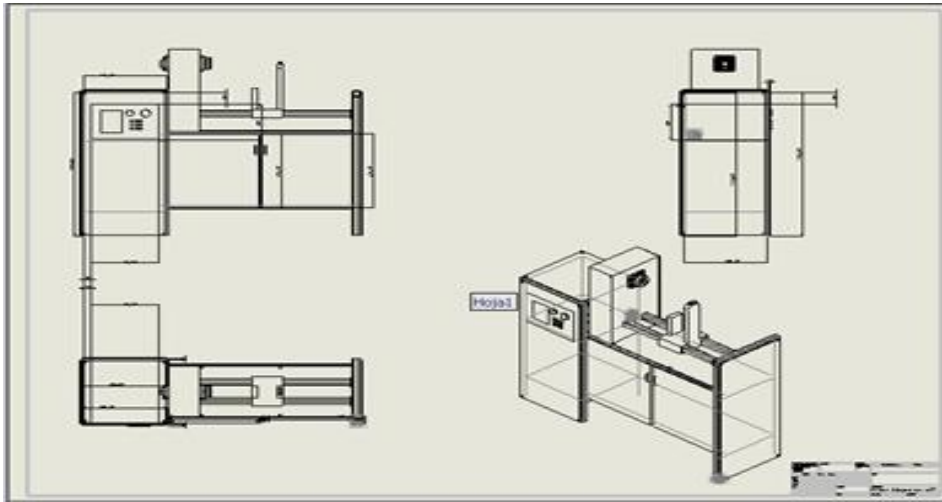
Dibujo en Solidworks con vistas frontal, lateral, superior y en 3D. Fuente: Autor
